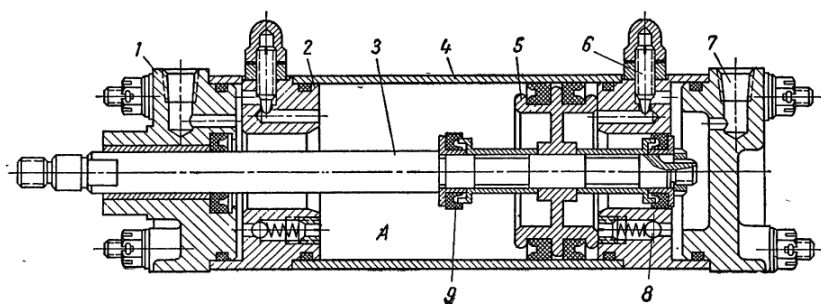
Двусторонний пневматический цилиндр с дроссельным устройством.
